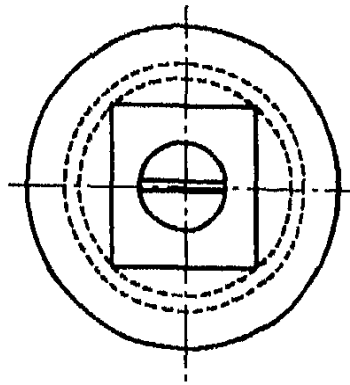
вид сверху вала с регулируемой высотой и верхняя пробка
